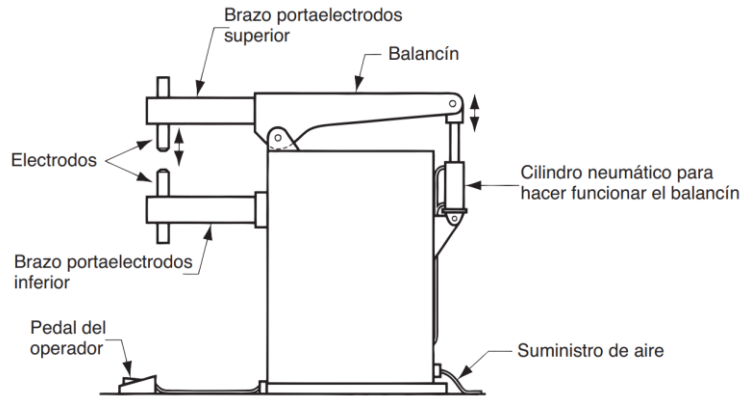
Máquina de soldadura de puntos por resistencia con balancín
